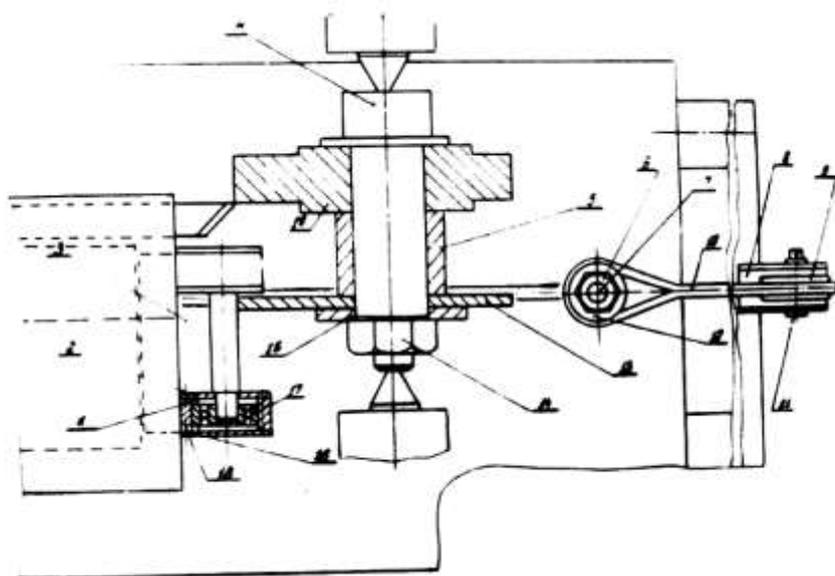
Схема приспособления для обработки кулачных шайб по копиру:
